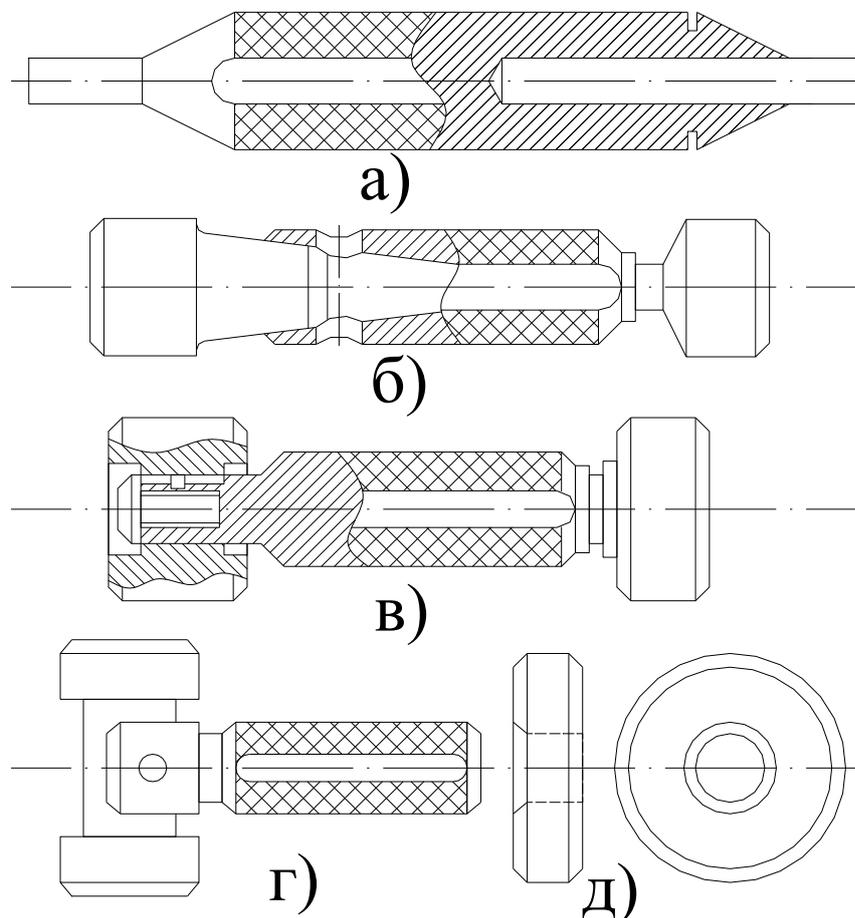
Основные типы калибр-пробок для контроля отверстий
